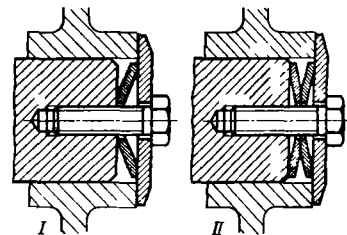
Стопорение пружинными шайбами болта, ввернутого в торец вала
